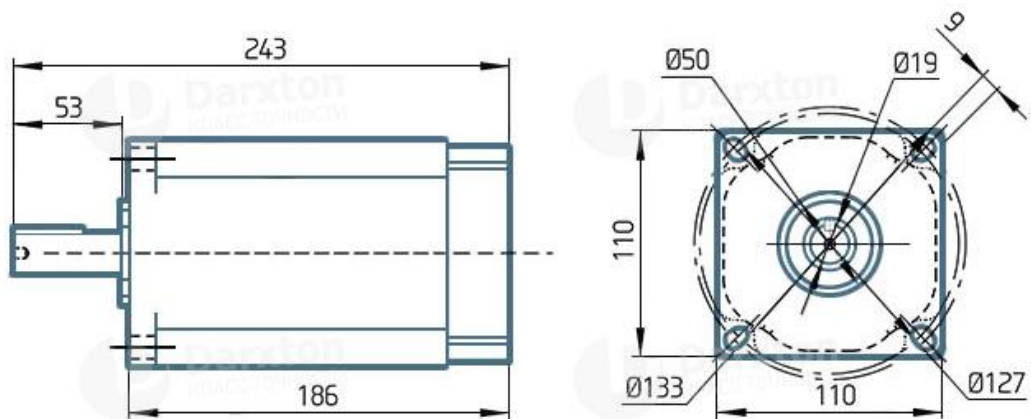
Схематичне креслення шагового двигуна ST110-150E
